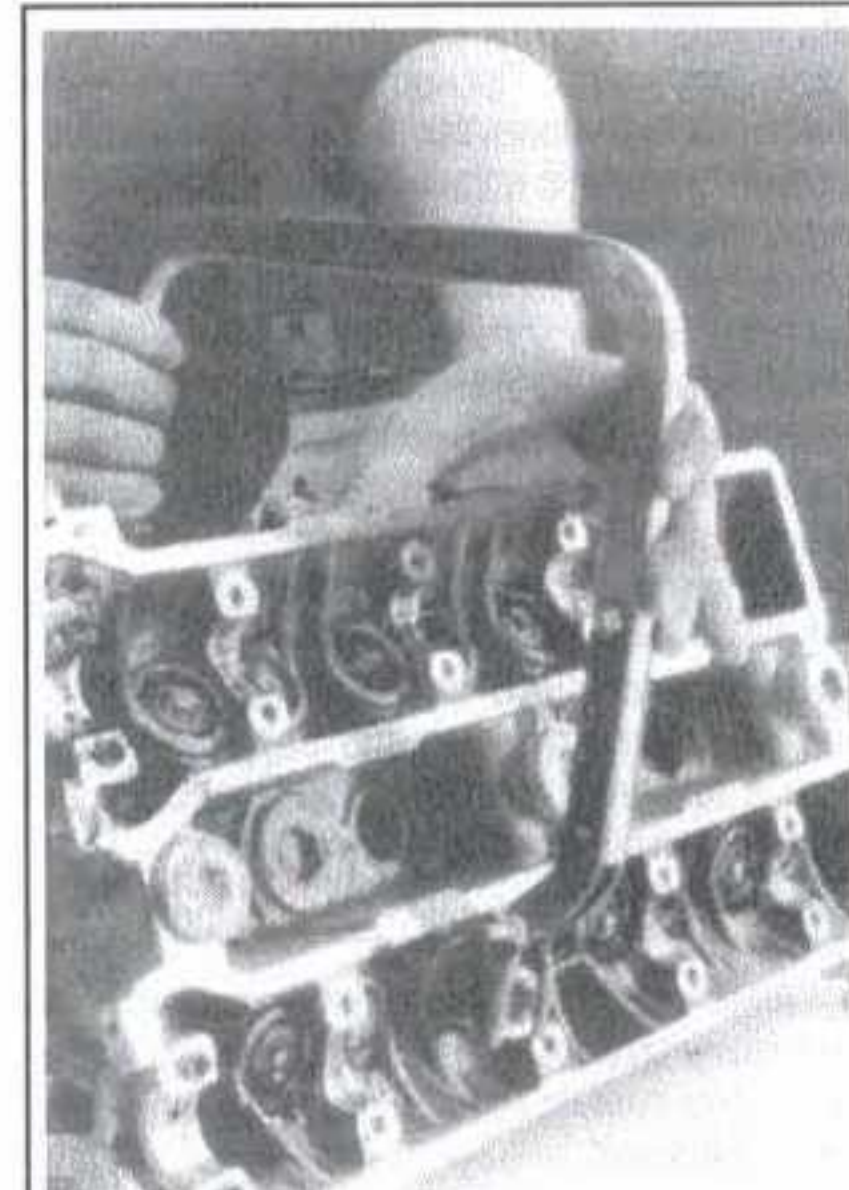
Установите съемник пружин для верхнего распределительного вала между захватами С-образного приспособления для сжатия пружин и тарелкой пружины, затем сожмите пружину
